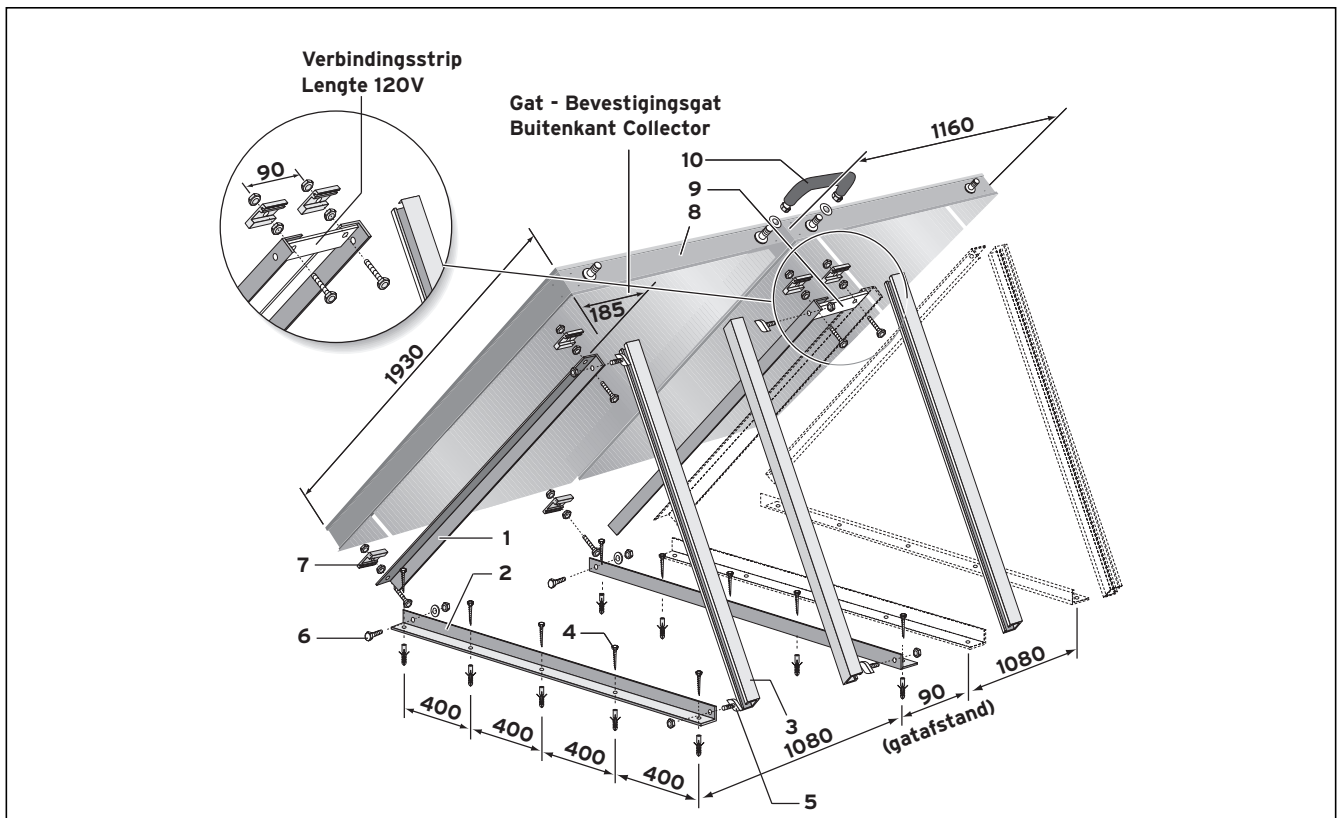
Module platdakmontage voor horizontale plaatsing van collectors
